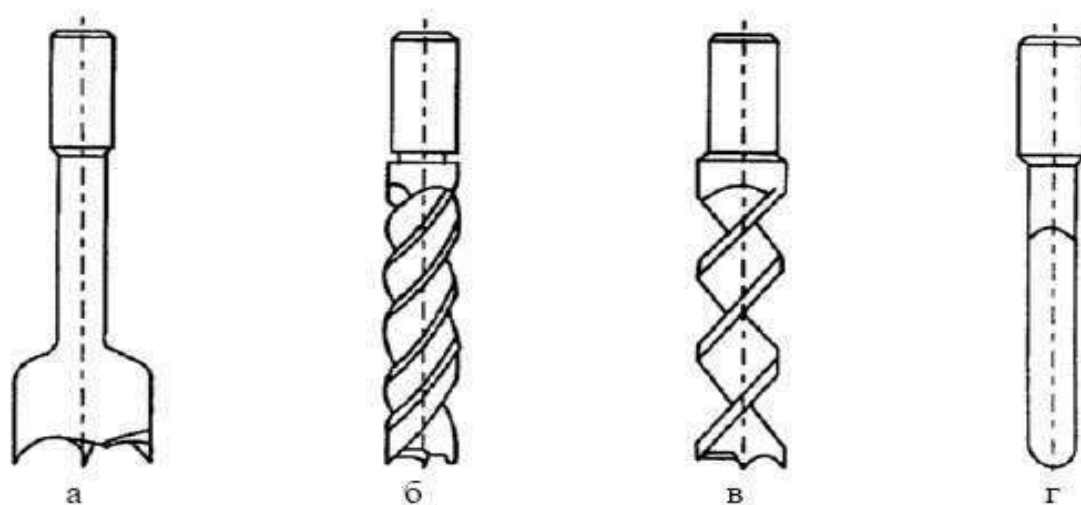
Сверла для обработки древесины: а – центровое с подрезателями; б – спиральное с подрезателями; в – винтовое; г – ложечное
